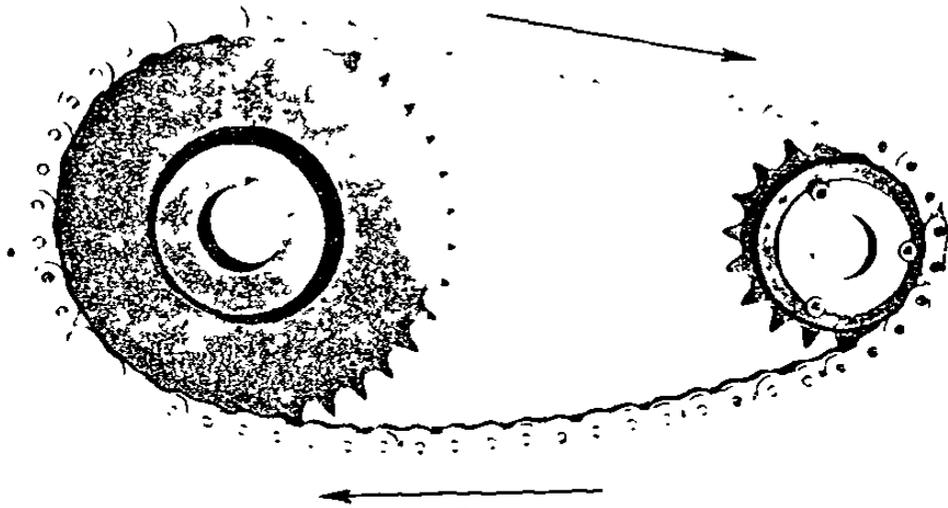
Montaje de una transmisión con cadena de rodillos.
